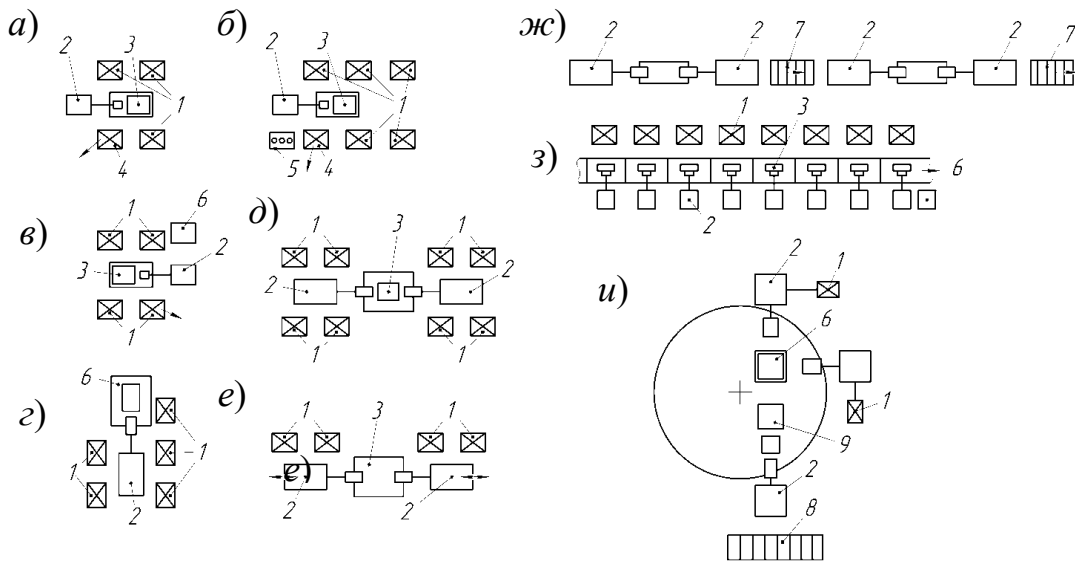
Примеры компоновочных схем РТК для сборочных операций
